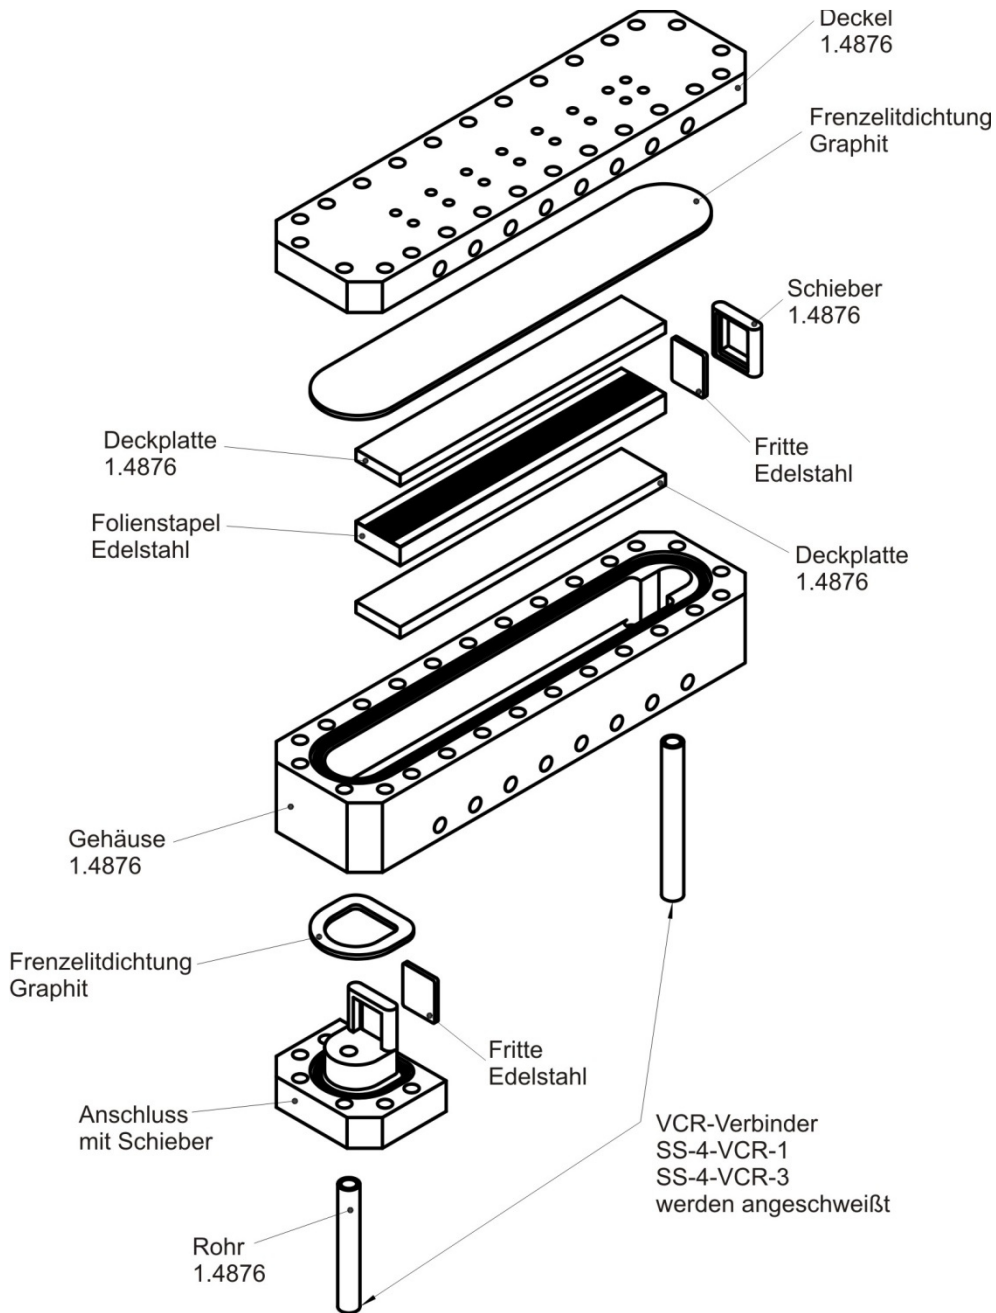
CAD-Explosionsbild des Reaktors.
